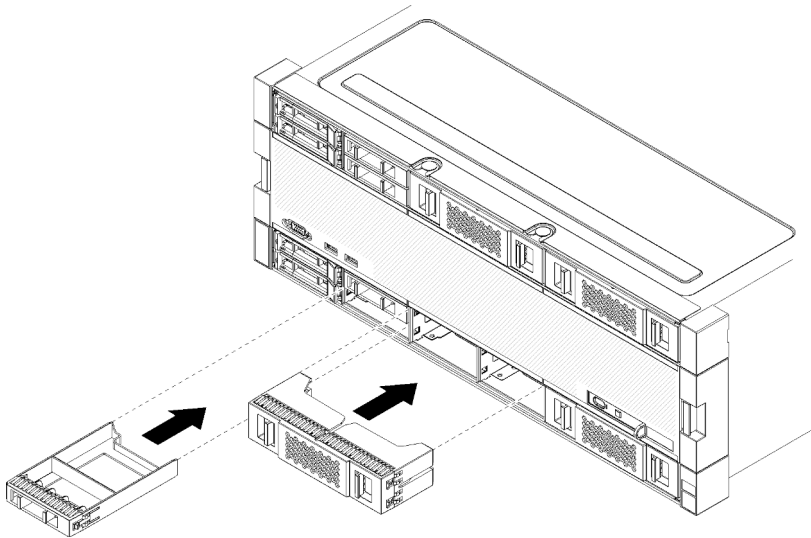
Installazione di un elemento di riempimento dell'unità disco fisso
